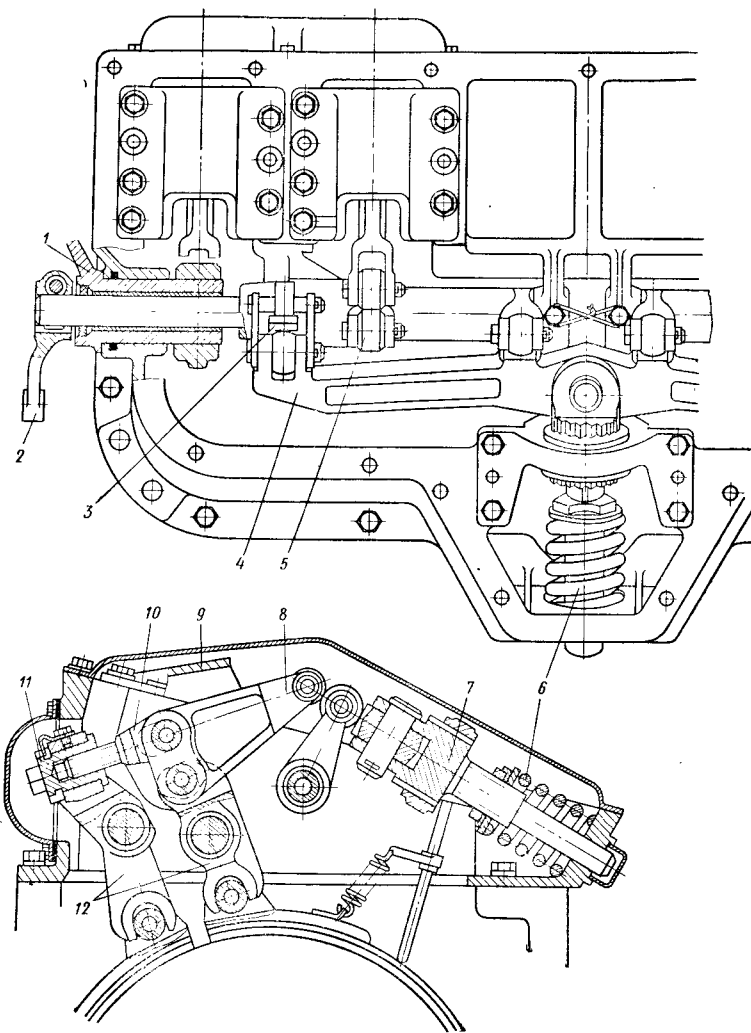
Тормоз планетарного механизма с центральной пружиной:
